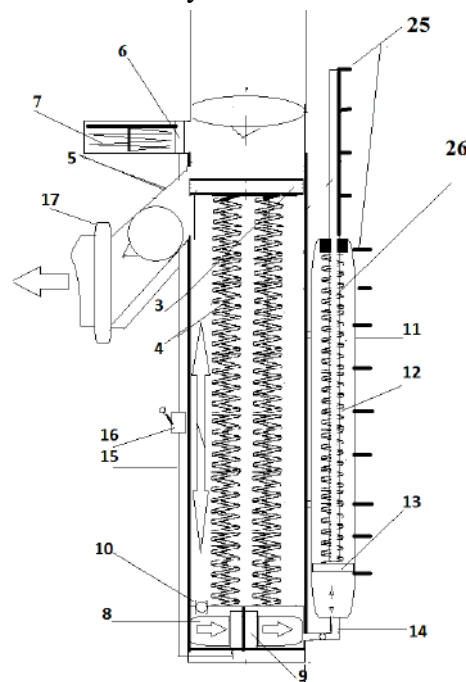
Схема розташування штока ручної корекції: 25 – скоби-сходи; 26 – шток ручної корекції
